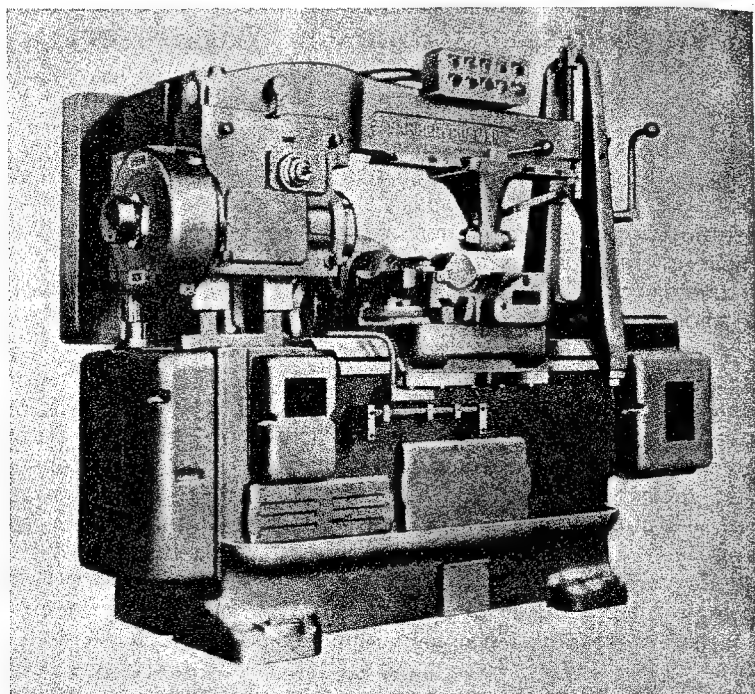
Máquina de tallar engranajes Barber-Colman.
